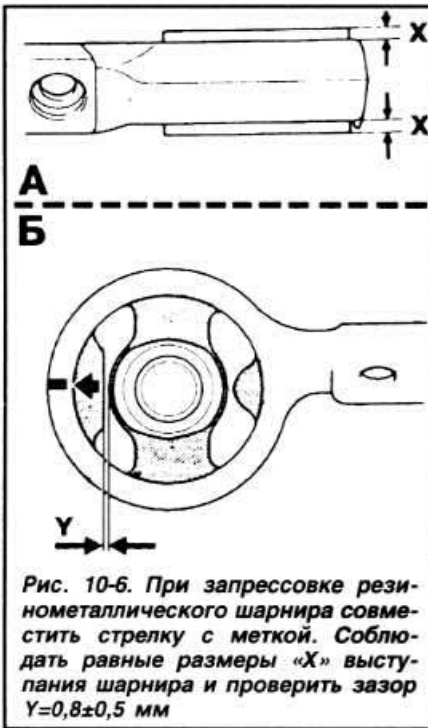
При запрессовке резинометаллического шарнира совместить стрелку с меткой. Соблюдать равные размеры «X» выступания шарнира и проверить зазор  $Y=0,8\pm 0,5$  мм
